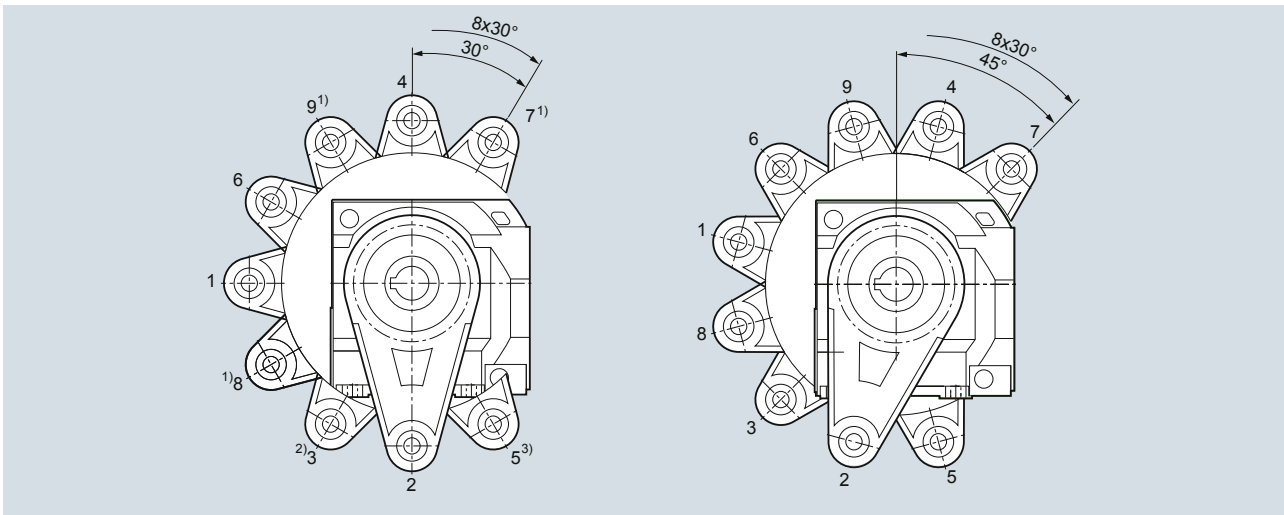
/9 Цилиндро-червячный редуктор С в насадном исполнении
